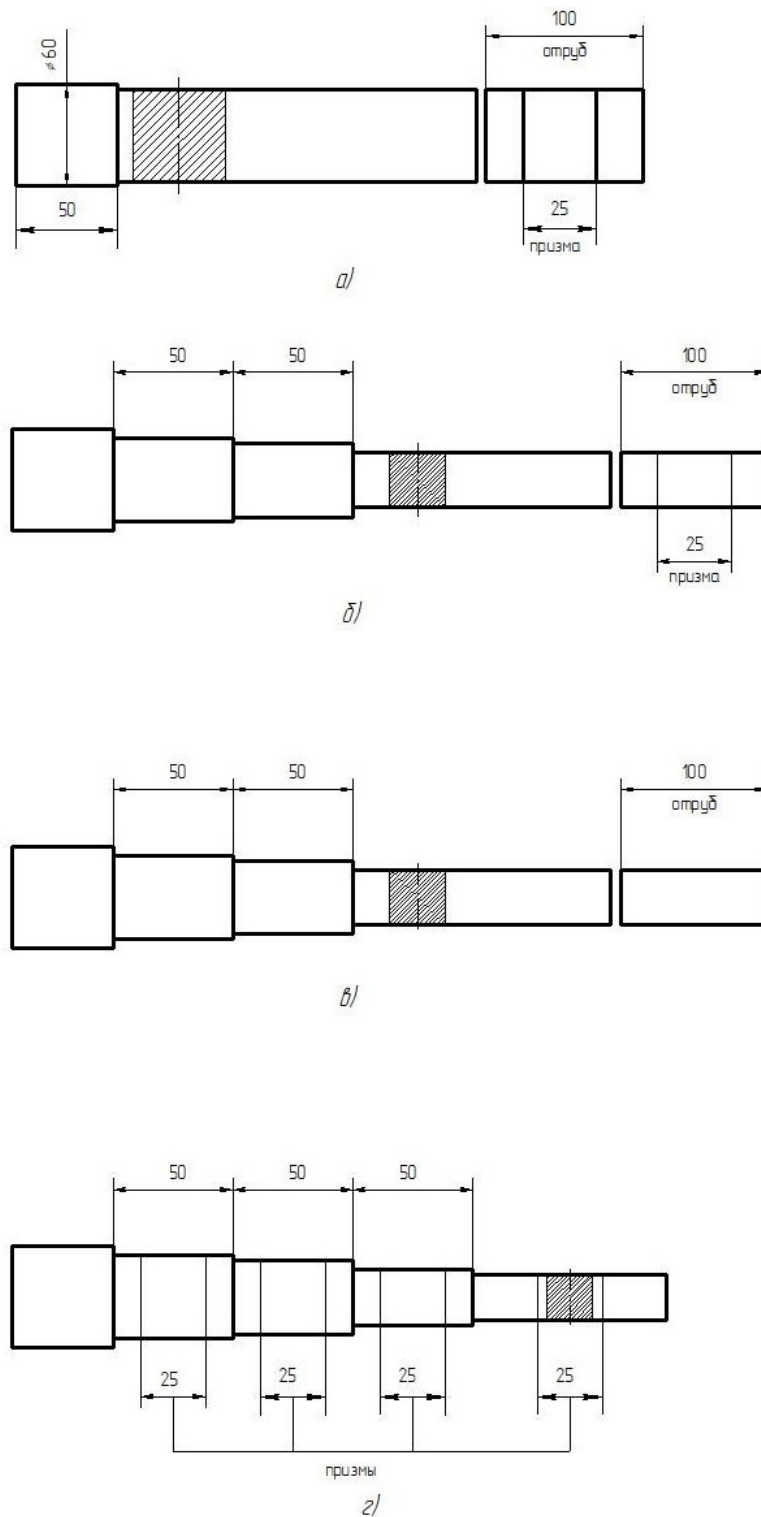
Переходы деформирования ступенчатой заготовки
